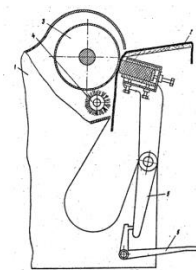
Схематическое изображение машины для шлифования и очистки кожи от пыли: 1 – машина для шлифования кожи, 2 – стол, 3 – барабан, 4 – щетка, 5 – педаль
